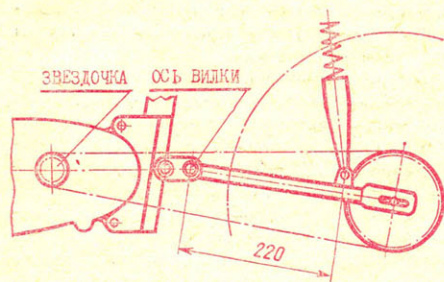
Взаимное расположение маятниковой вилки и двигателя.
